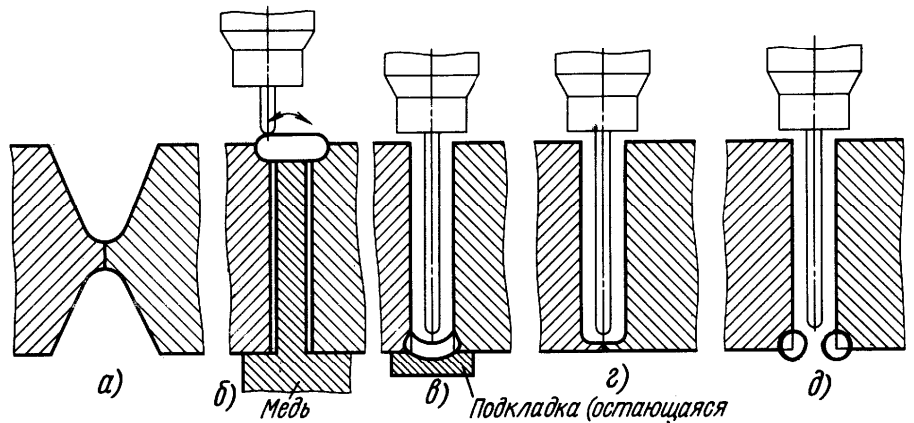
Подготовка кромок под многослойную сварку: а—обычная разделка; б...д—щелевая
